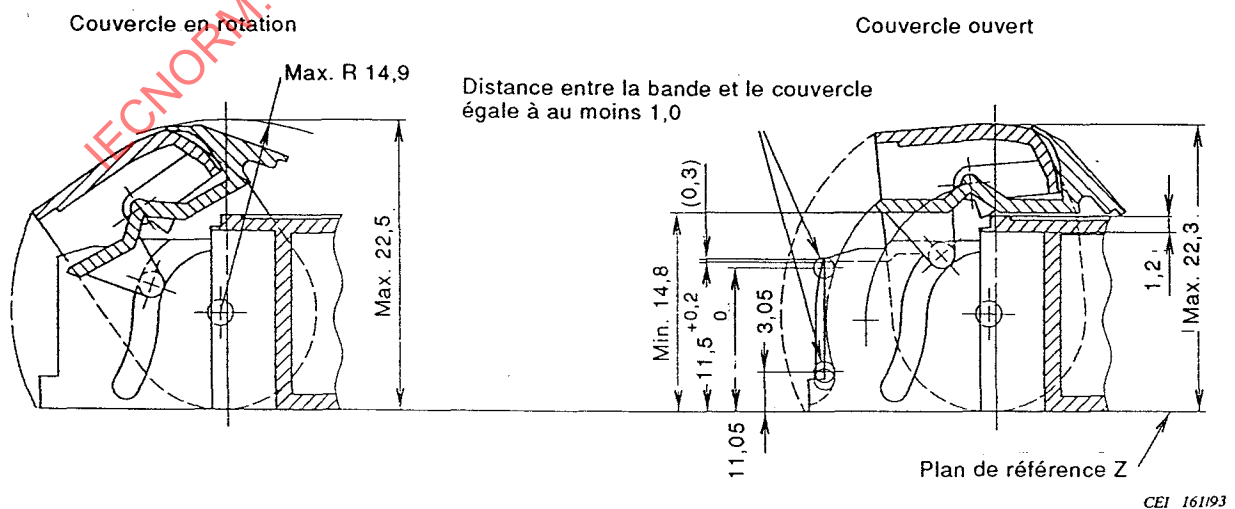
Dimensions maximales du couvercle (vue latérale)
